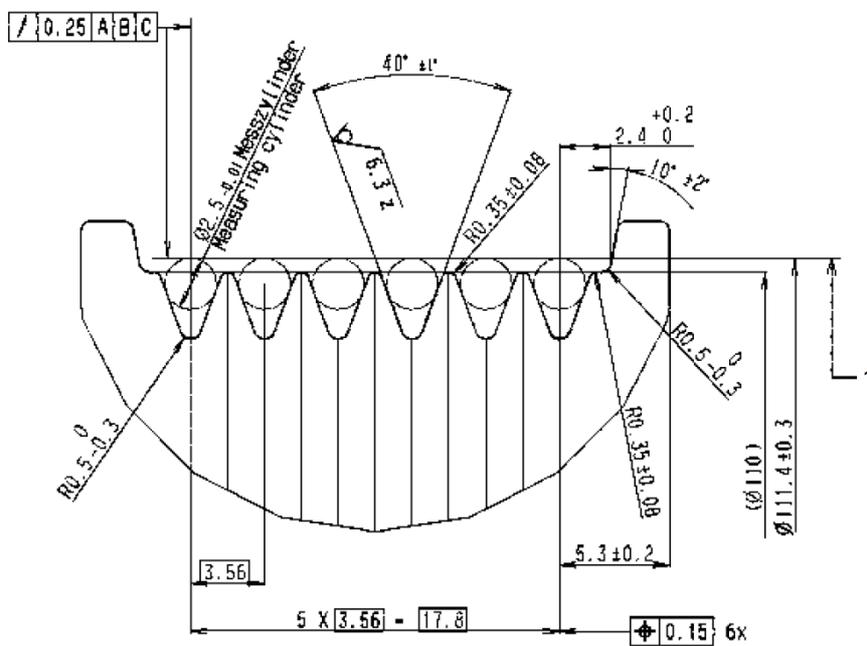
Детальное изображение U — Шкив компрессора климатической установки, диаметр шкива: 110 мм.
